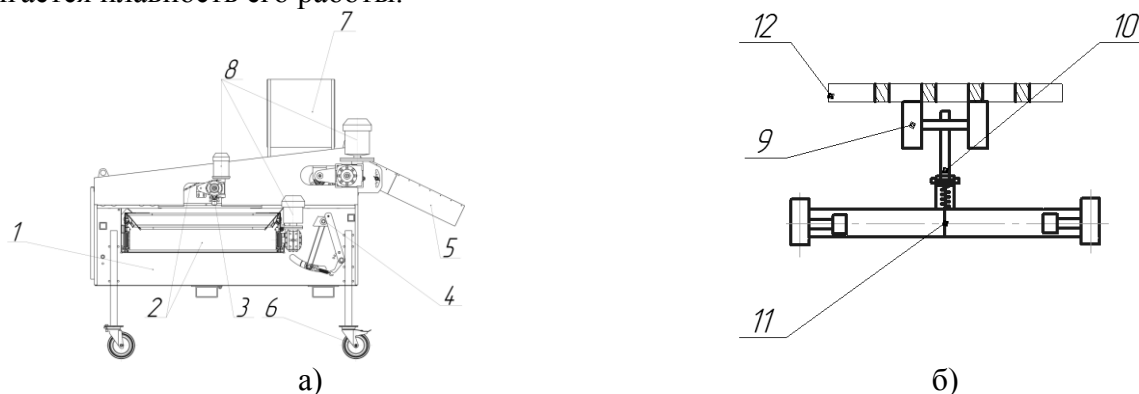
Схема машины для калибровки картофеля: а – общий вид; б – схема расположения роликов встряхивателя
